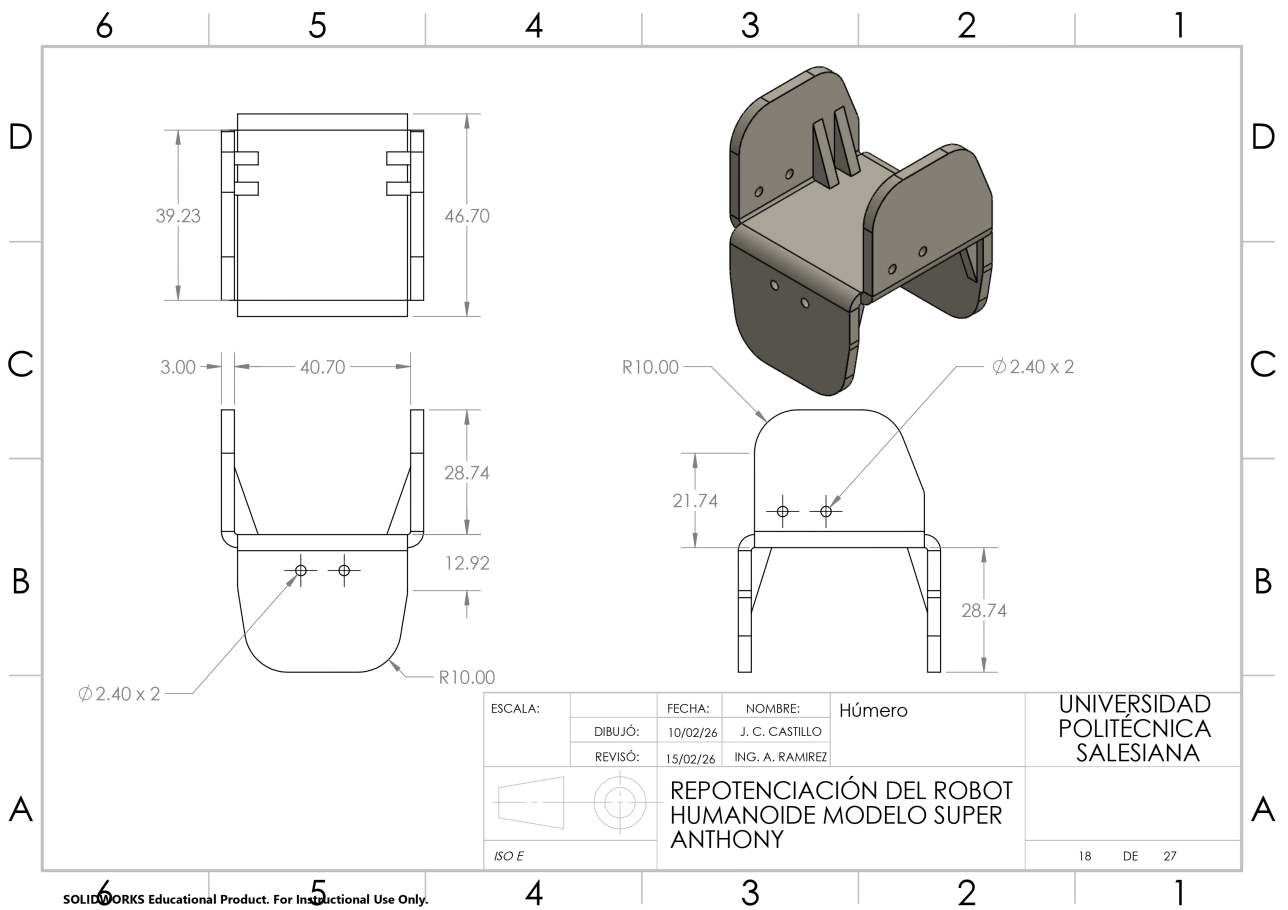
Lámina acotada del húmero del robot humanoide, por J. Castillo y B. Gualle, Solidworks
